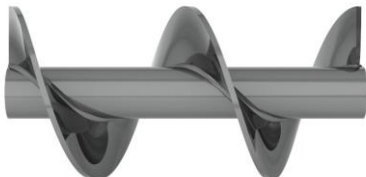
Типовий вертикальний гвинтовий конвеєр фірми KWS [165]
